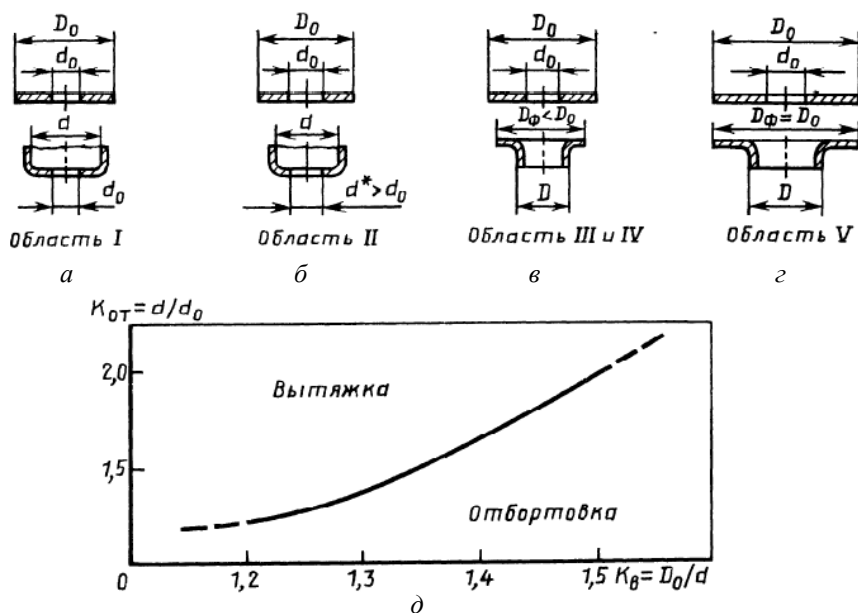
Деформирование плоских кольцевых заготовок: а – г – варианты формоизменения; д – разделение области отбортовки и вытяжки
